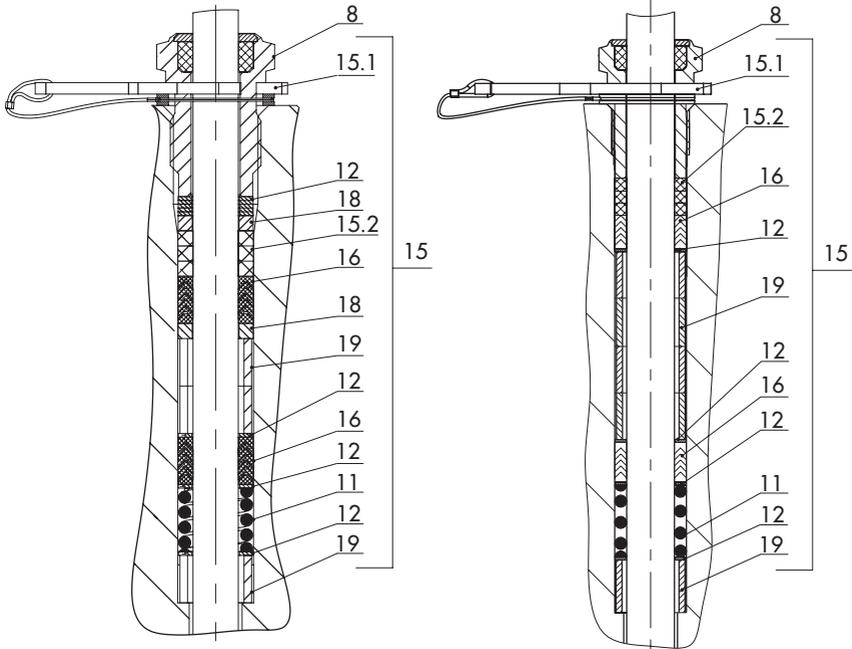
Empaquetadura estándar: DN 15...40 (izquierda) y DN 50...100 (derecha)
